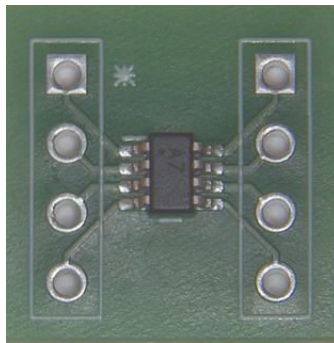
分离下来的 PCB 上已焊接 IC
